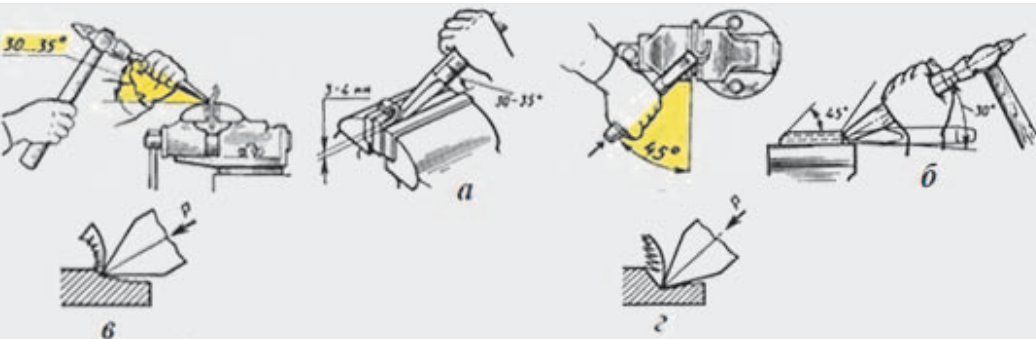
Прийоми рубання металу: а — за рівнем губок лещат; б — за розмічальними рисками; в — при малому куті нахилу зубила; г — при великому куті нахилу зубила
